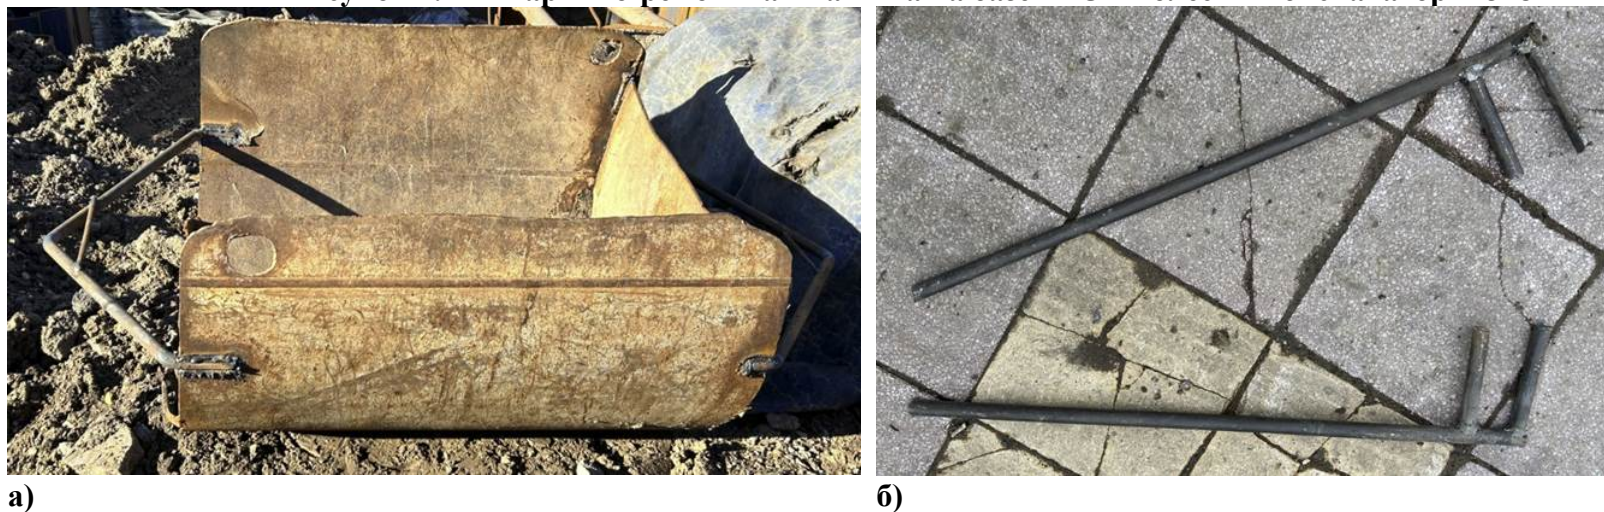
Скребковое приспособление для прочистки трубопровода и ключи для скрутки резьбовых модулей
